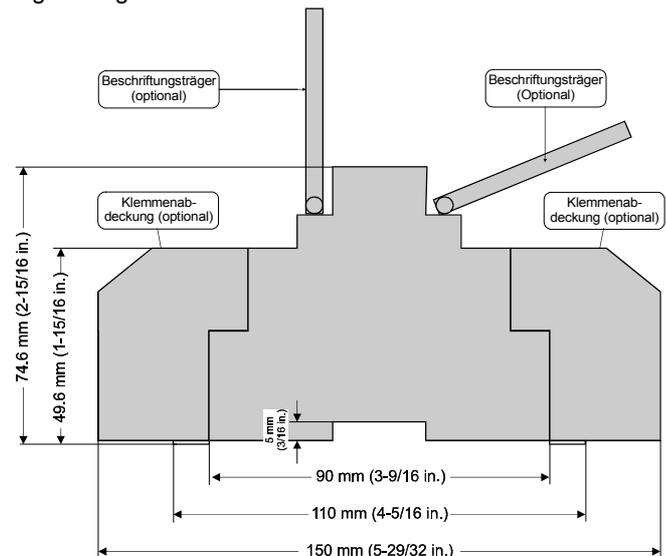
Excel 12 Gehäuse (Seitenansicht)
